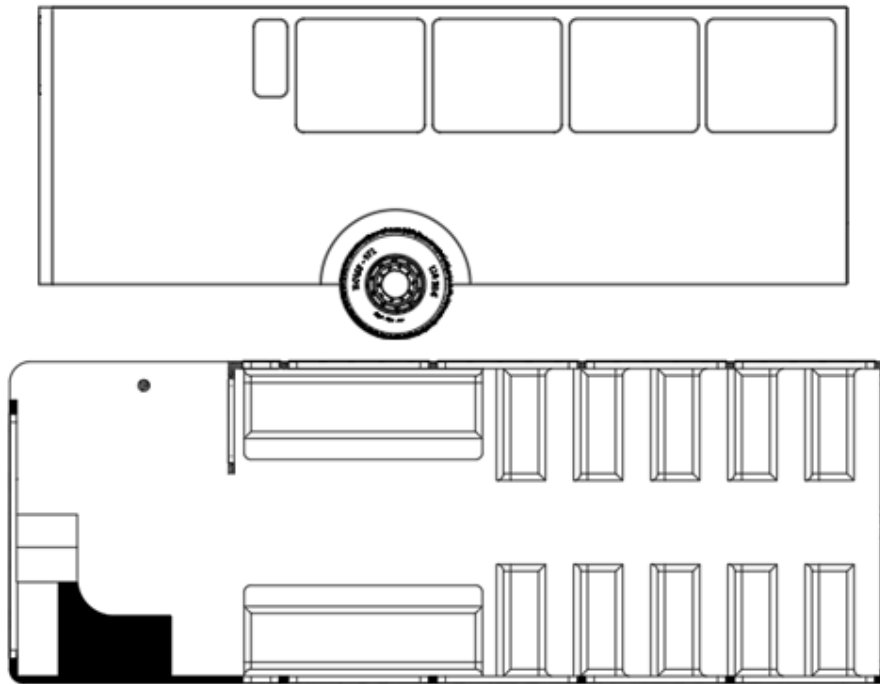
Vistas diseño planta inferior. Fuente propia
